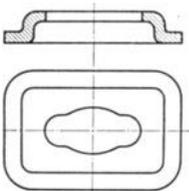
Schnittplatte aus hohlgepreßtem Werkzeugstahlblech.
